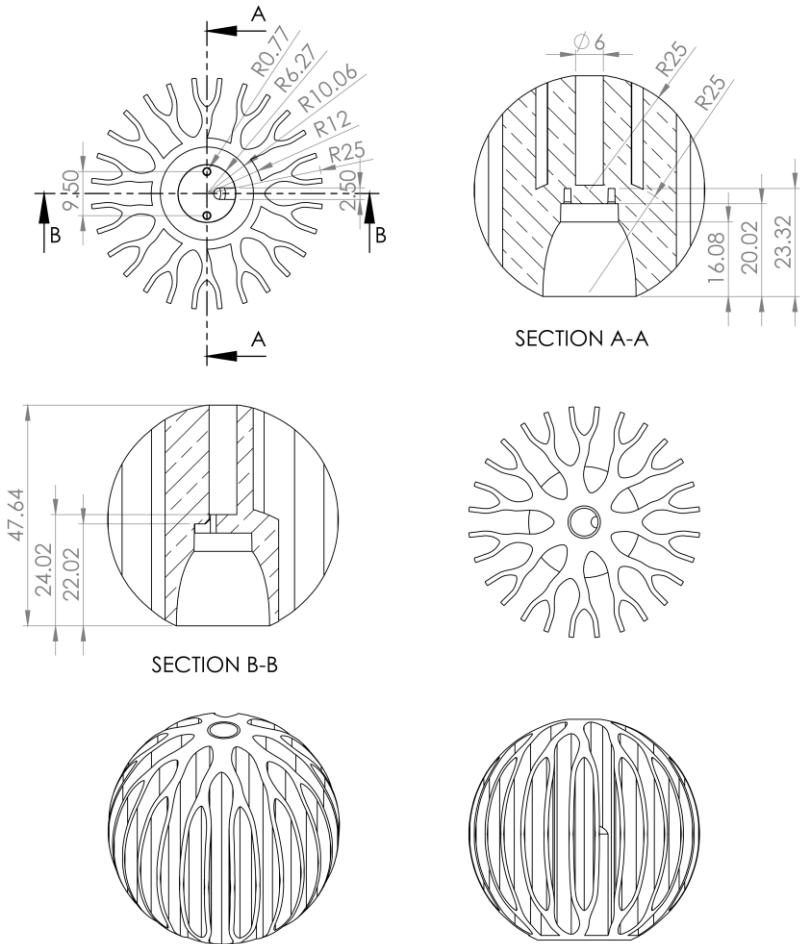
Bemaßte Zeichnung verzweigter Leuchten-Kühlkörper
